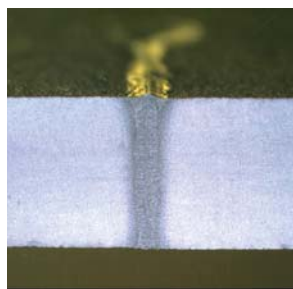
Soudure laser en bout-à-bout sur acier de 12 mm
